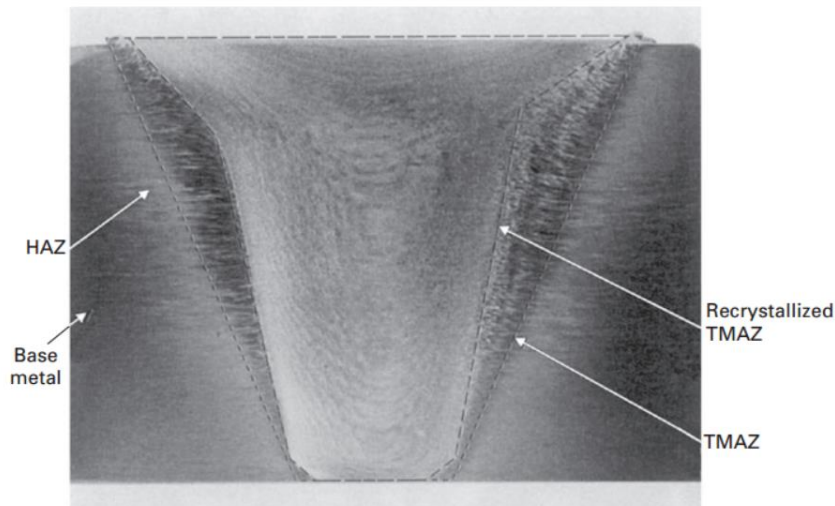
4 zonas típicas en sección transversal de soldadura FSW. 25.4mm de espesor en aluminio 2195 [11].
